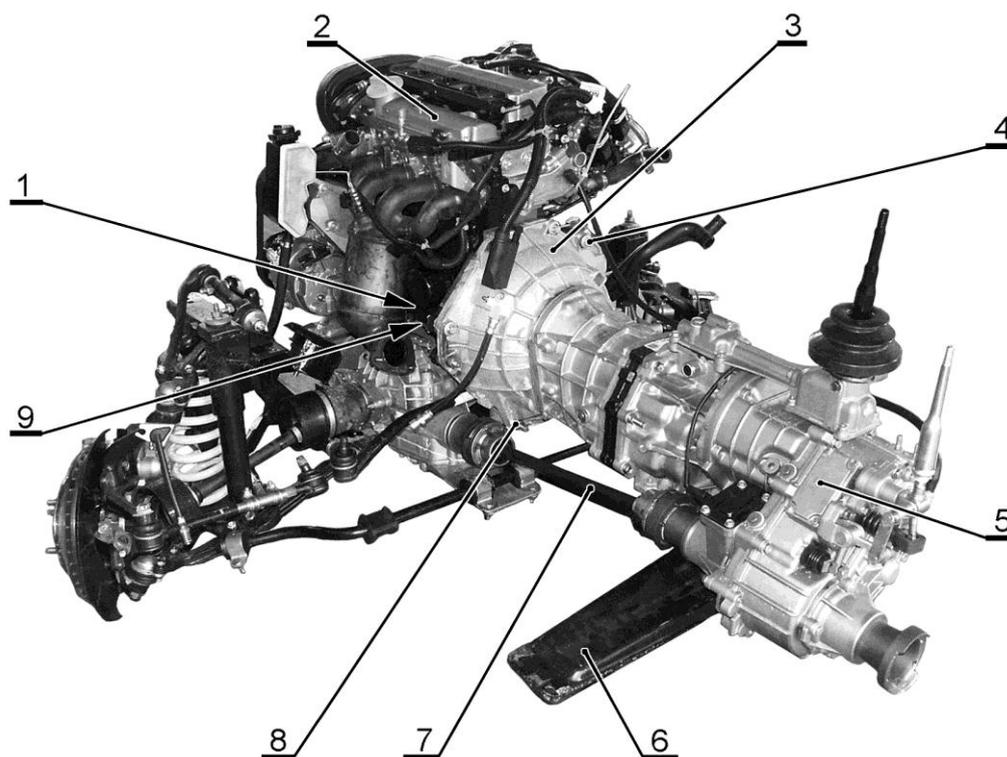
Снятие коробки передач с раздаточной коробкой в сборе:
